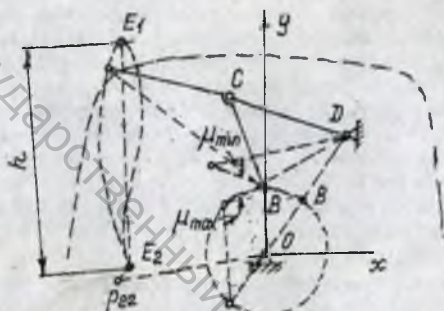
Схема шарнирного механизма нитепритягивателя
